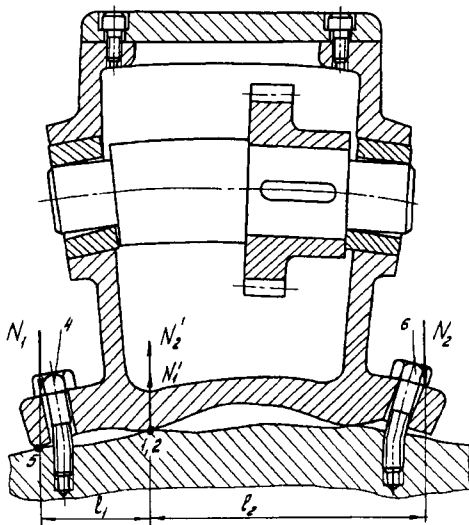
Характер деформирования деталей редуктора при закреплении
